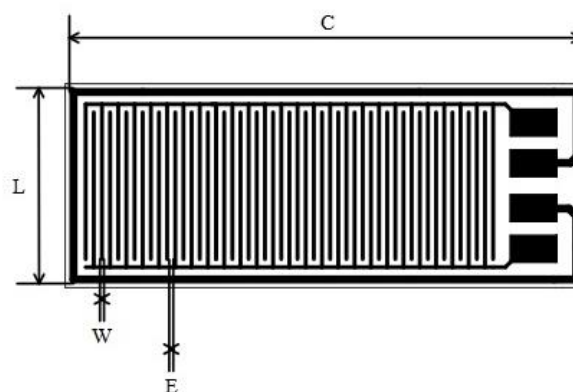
Desenho esquemático do sensor projetado em KiCad.
